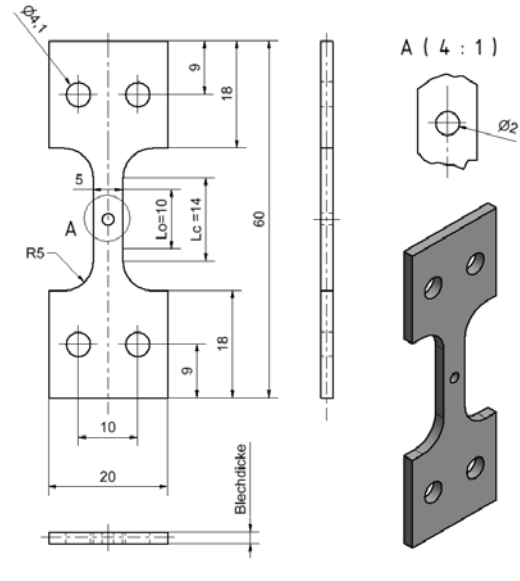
Geometrie der Zugproben mit einem Loch in der Probenmitte
